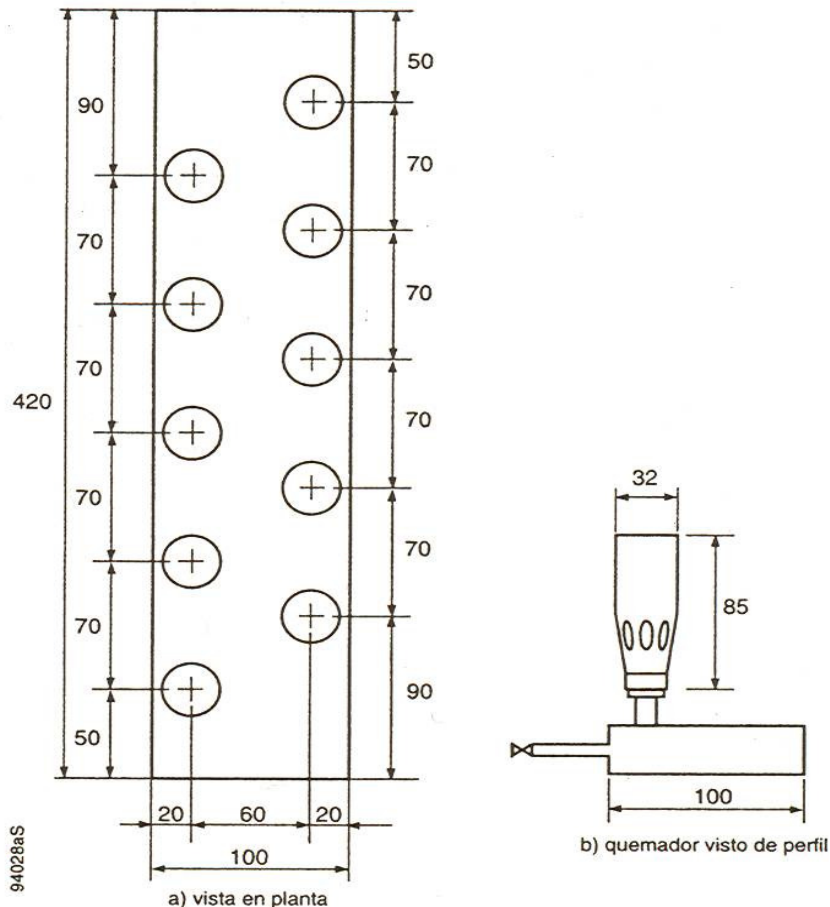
Ensayo de resistencia al fuego: montaje del quemador múltiple (mm)
